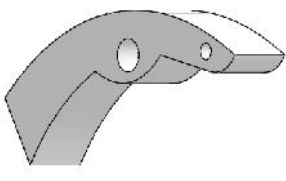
Despiece del conjunto de la Rueda imperial en SolidWorks
